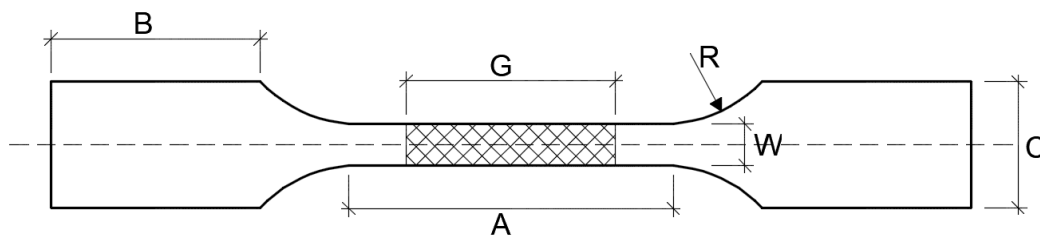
Dimensiones de las probetas según ASTM A370.
